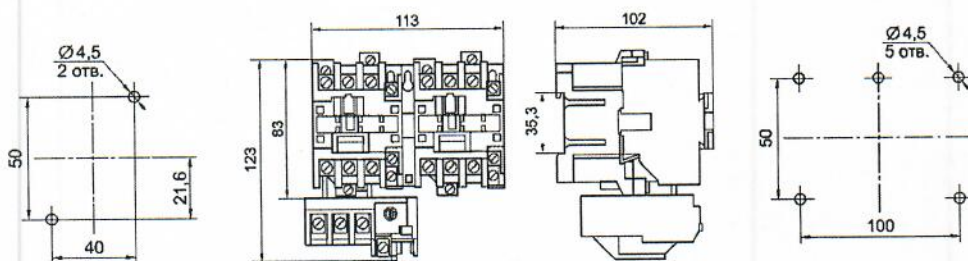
Пускатель реверсивный ПМ12-025 25А.
